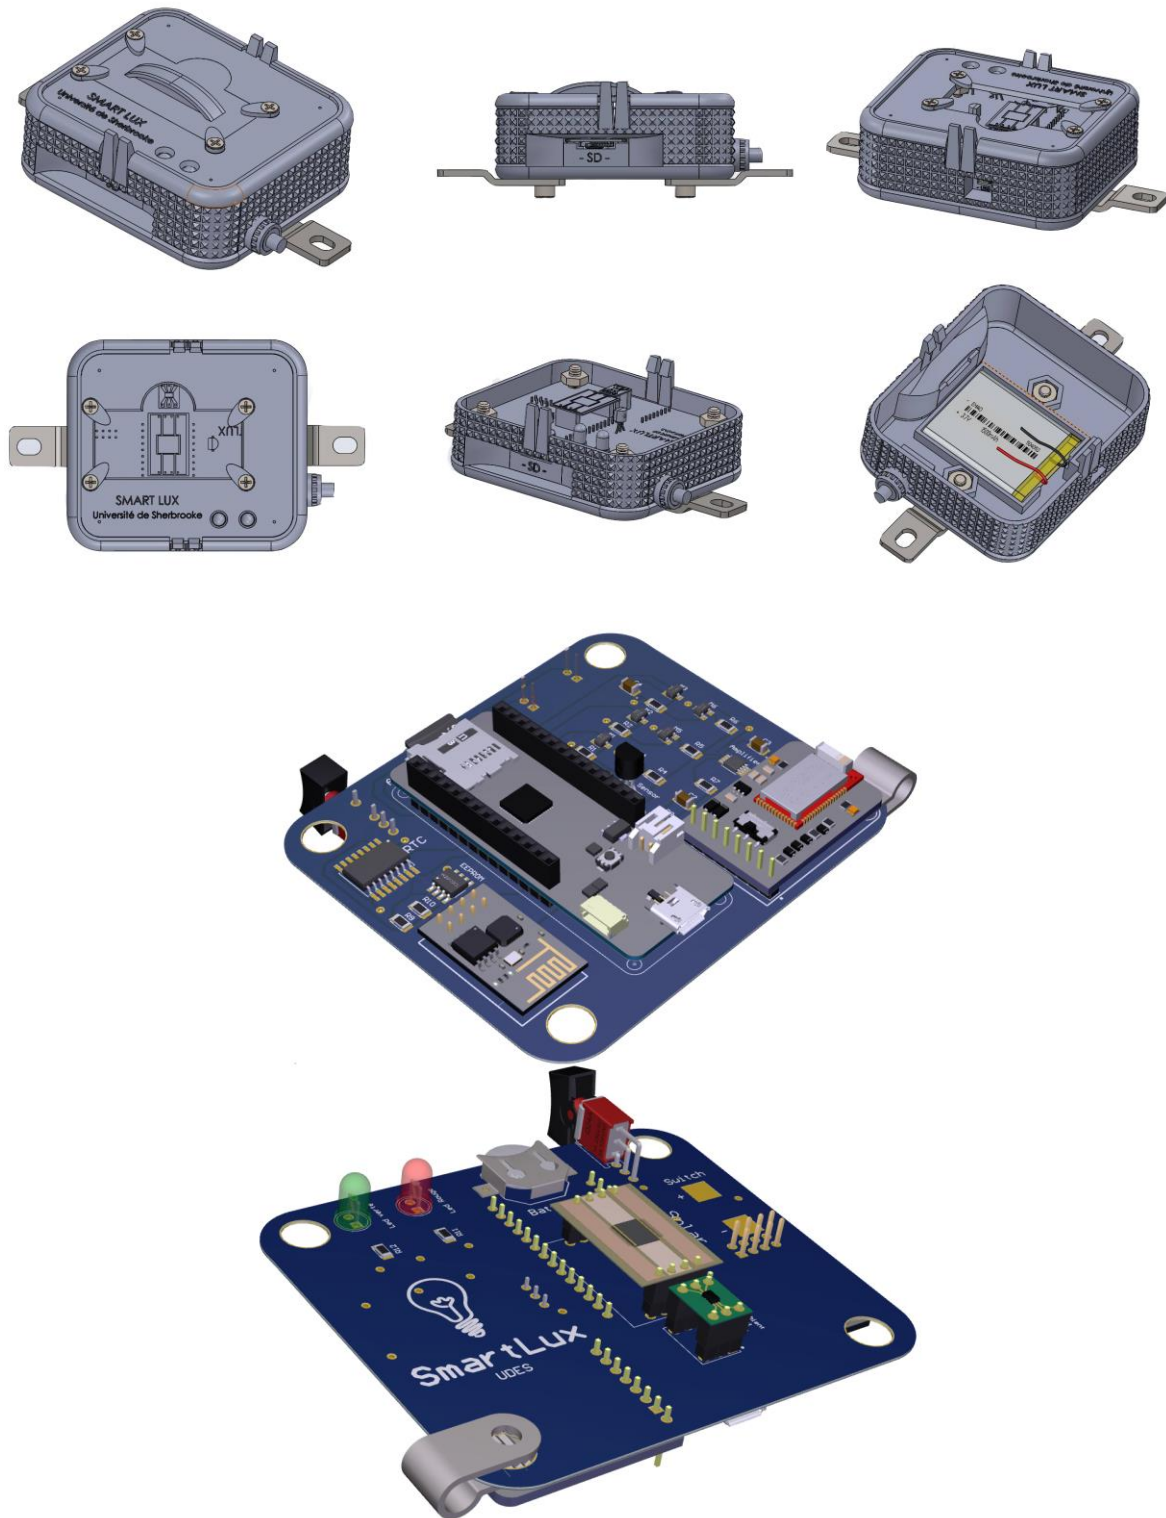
Module complet assemblé (en haut) et PCB (en bas) modélisés sur SolidWorks
